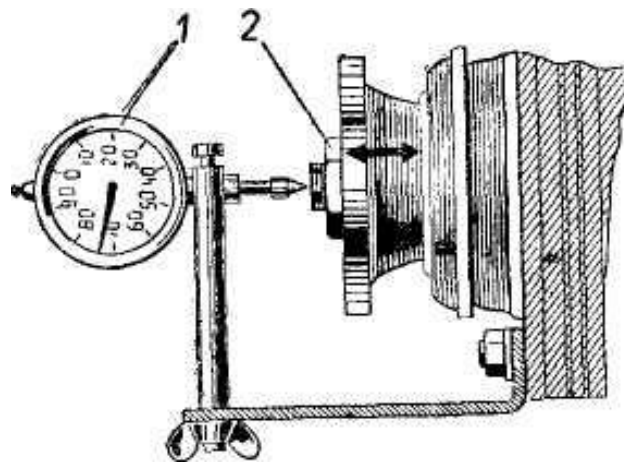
Перевірка осьового зазору підшипників за допомогою індикатора
